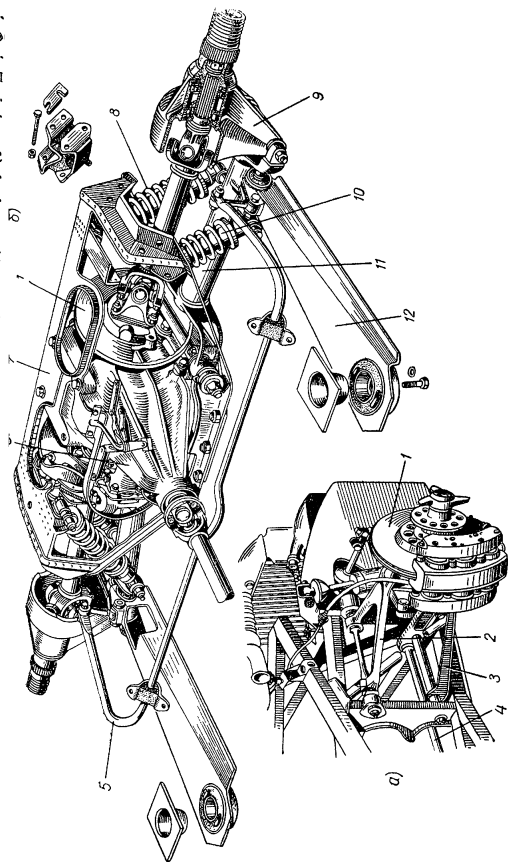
Подвеска автомобиля «Ягуар»: а — передняя; б — задняя; 1 — дисковый тормоз; 2 — верхний рычаг; 3 — нижний рычаг со смещенным креплением торсиона; 4 — торсион; 5 — стабилизатор; 6 — картер главной передачи; 7 — скобообразная поперечина; 8 — пружина; 9 — кронштейн для размещения подшипников колеса; 10 — амортизатор; 11 — вилчатый рычаг подвески; 12 — реактивная штанга
